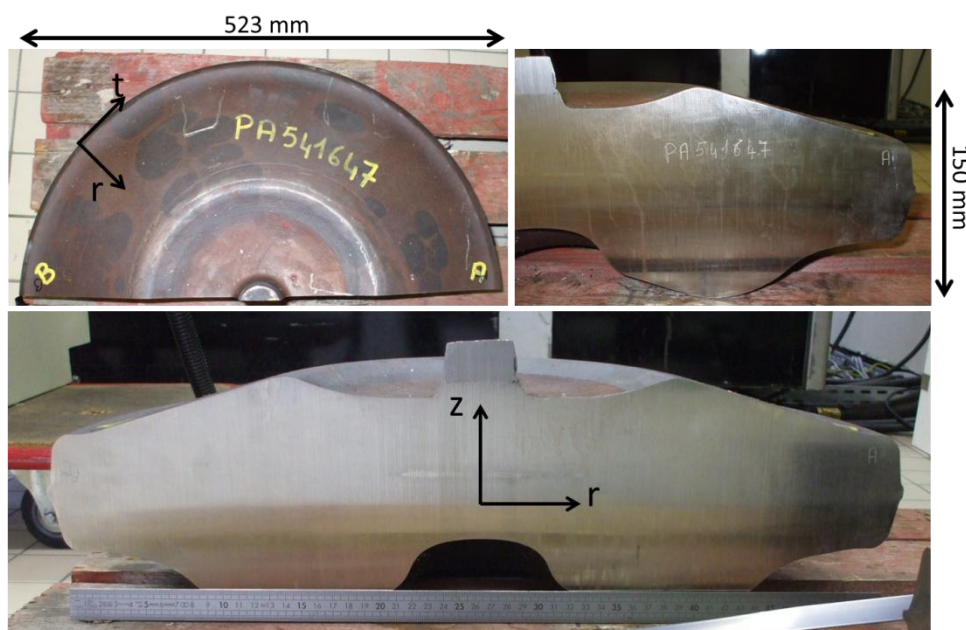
Brut de forge pour usiner un disque de turbine HP
